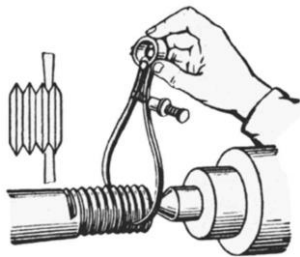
Вимірювання внутрішнього діаметра різьби кронциркулем із гострими ніжками
